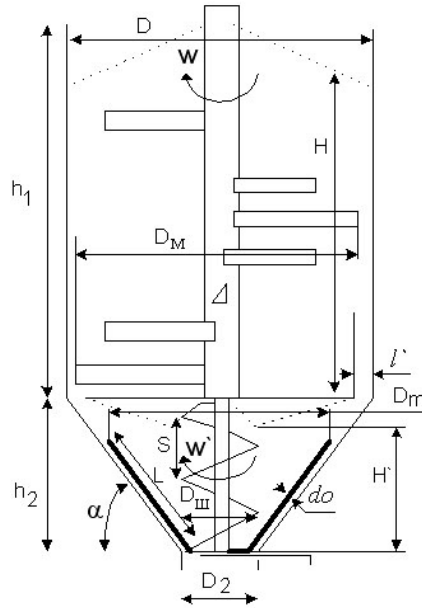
Схема используемых обозначений размеров смесителя-дозатора
